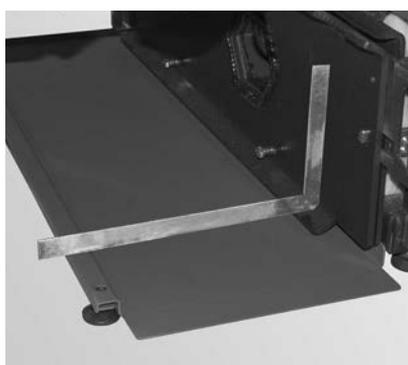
Allineare il pannello a pavimento ad angolo retto
